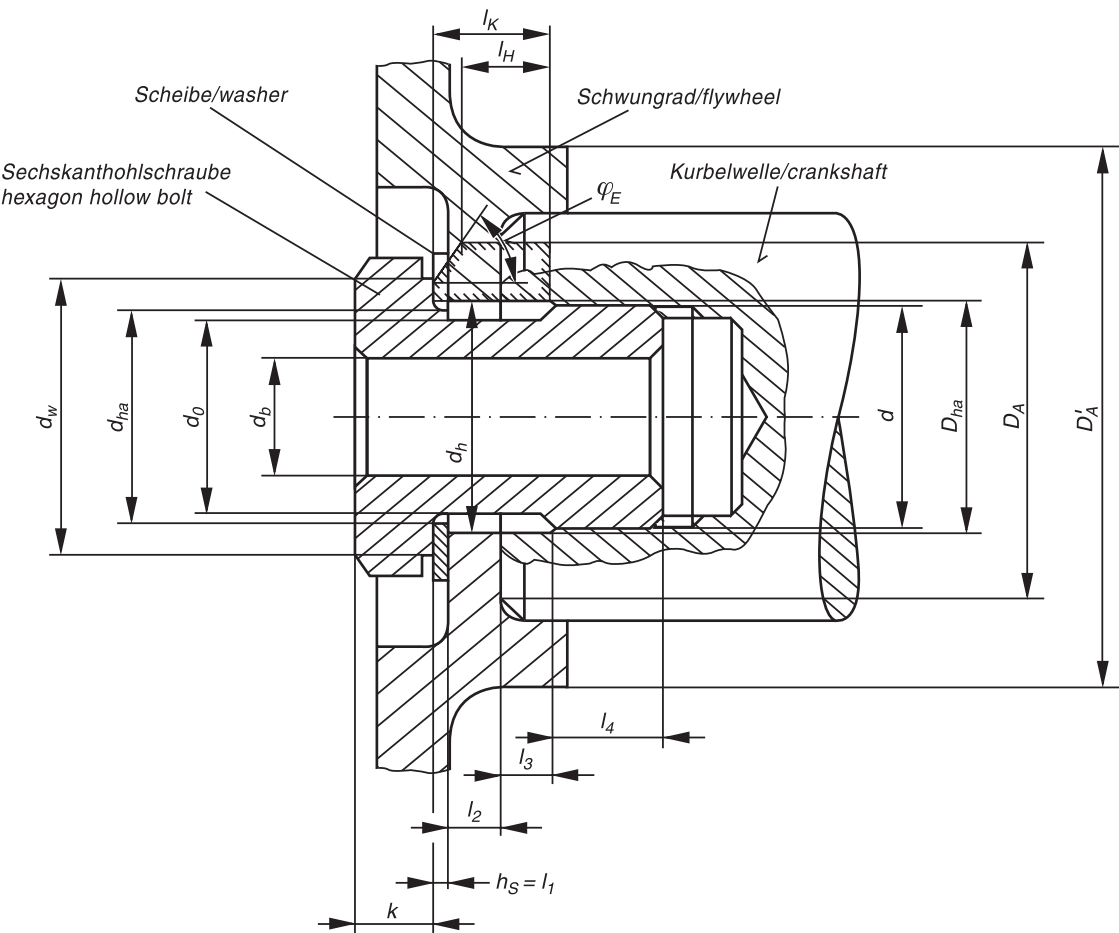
/1. Schwungradbefestigung mittels Zentralschraube
